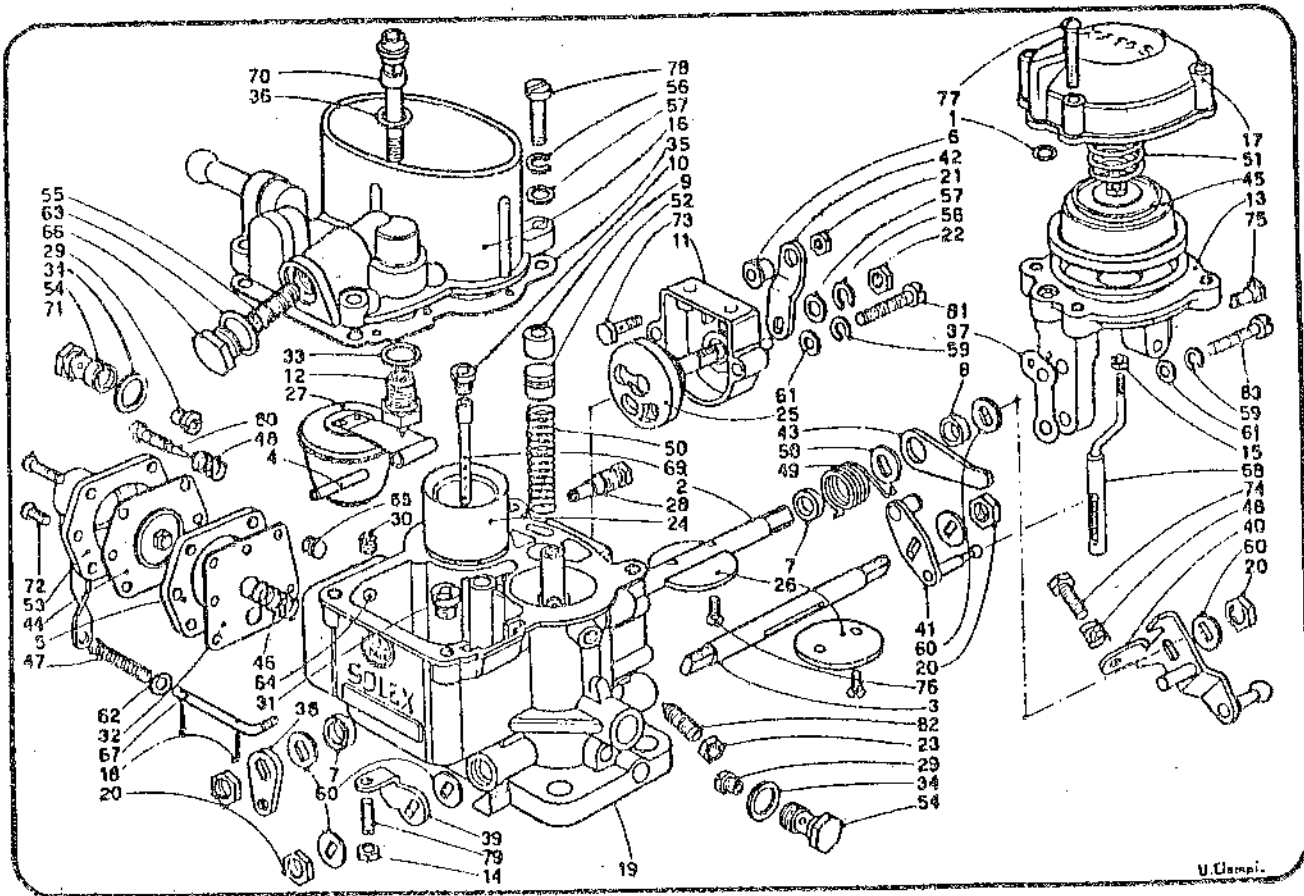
/36 - Carburateur (type Solex). (Du Catalogue P. D.)
